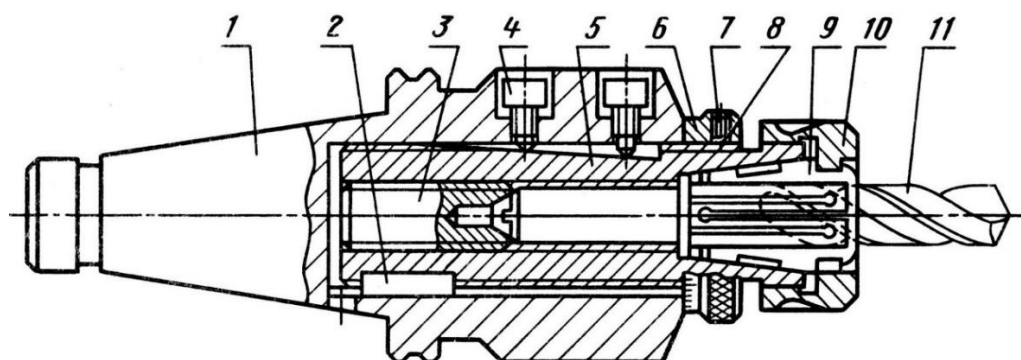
Сборочный чертеж АСП : 1 - базисный агрегат с конусом 7:24; 2 – шпонка; 3 – упор; 4 – винт; 5 – сменная наладка; 6 – регулировочная гайка; 7 – стопорный винт; 8 – подкладка; 9 – цанга; 10 – зажимная гайка; 11 – режущий инструмент
